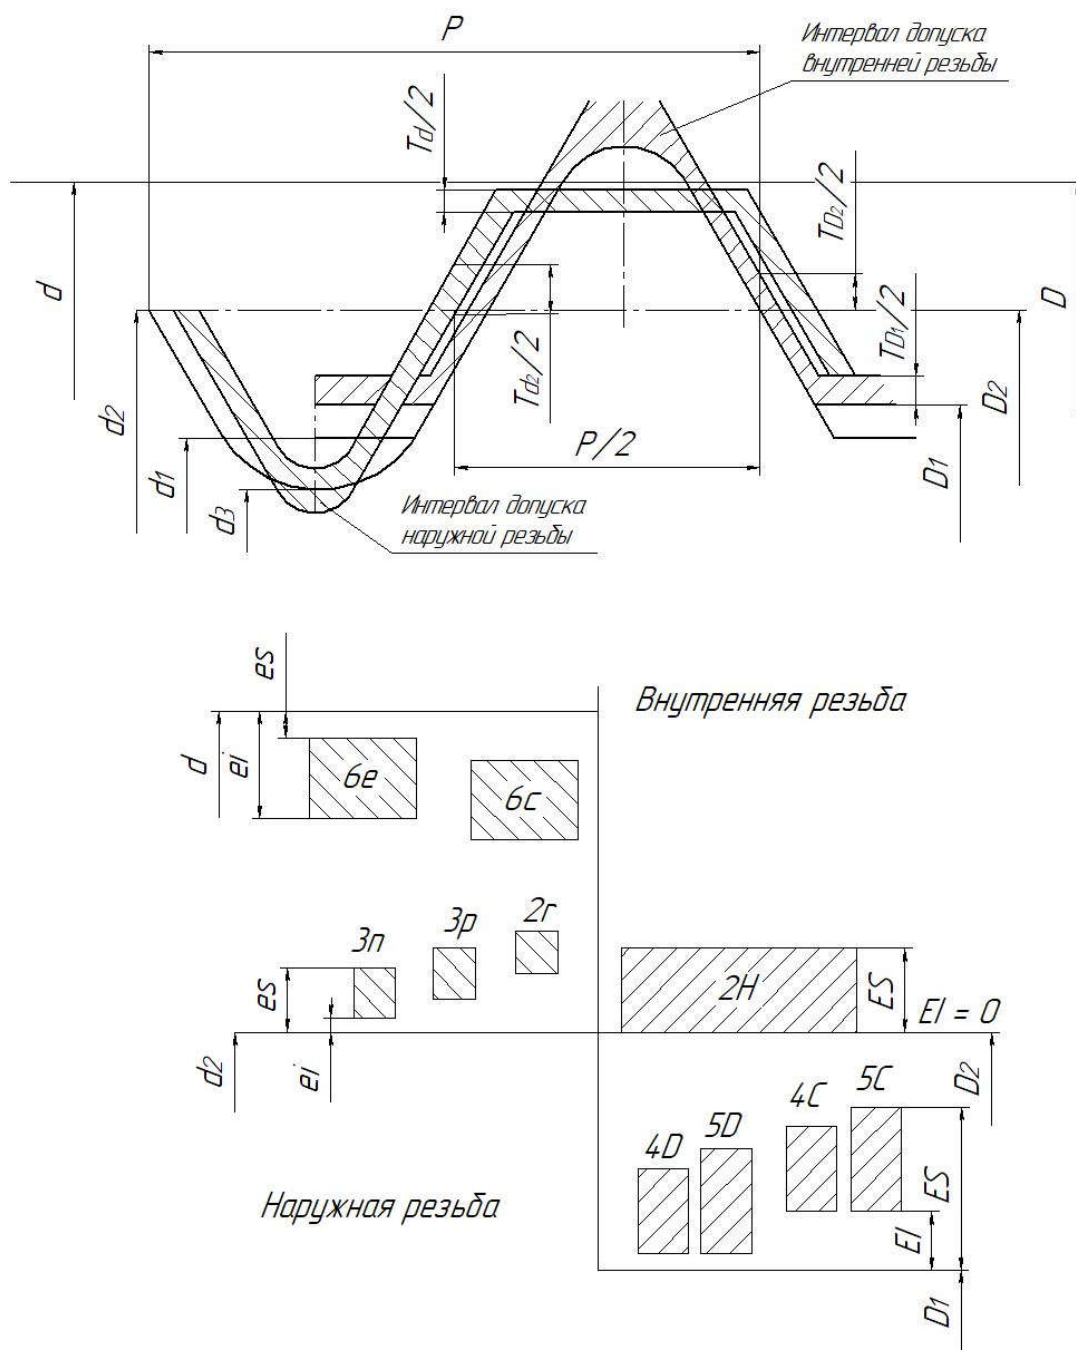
Расположение интервалов допусков наружной и внутренней резьбы для посадки с натягом по [32]
